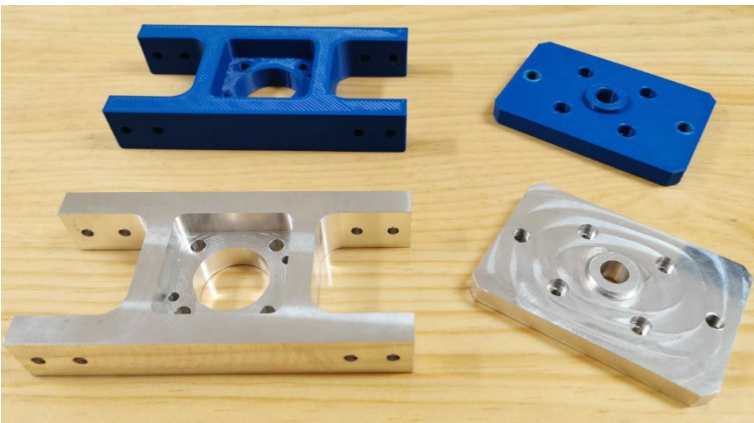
Piezas de soporte hechas en PLA y aluminio
